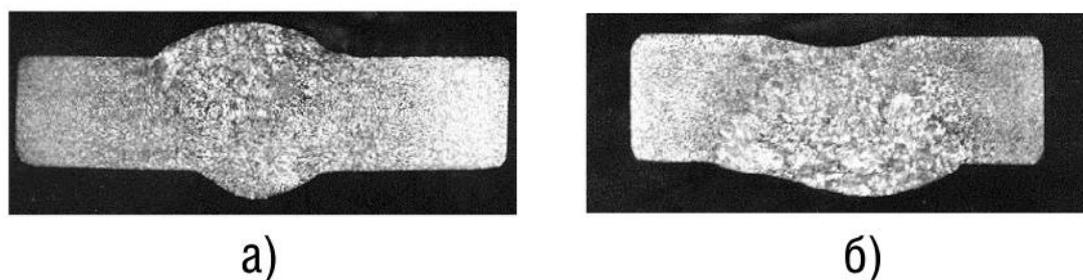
Характерные формы сечений сварных соединений трубопроводов обвязки при сварке в нижнем (а) и потолочном (б) положении
